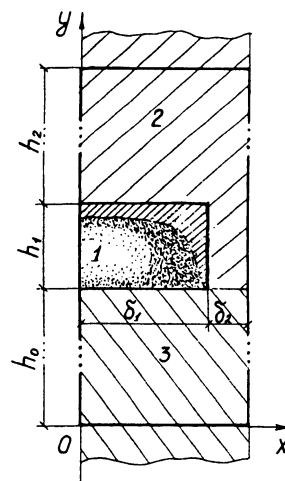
Схема к расчету затвердевания элементов аккумуляторной решетки при непрерывном литье: 1 — отливка; 2 — формообразующий валок; 3 — башмак
